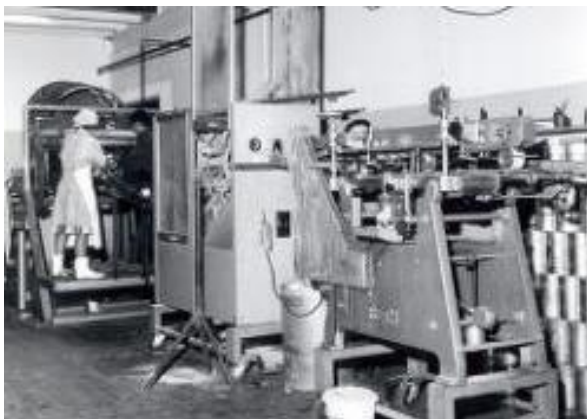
Uitsorteren en etiketteren (begin jaren '60)
